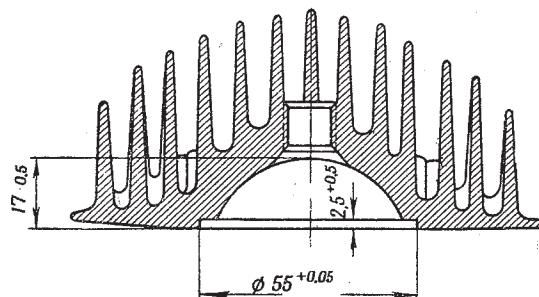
Головка двигателя спортивного мотоцикла К-125С
